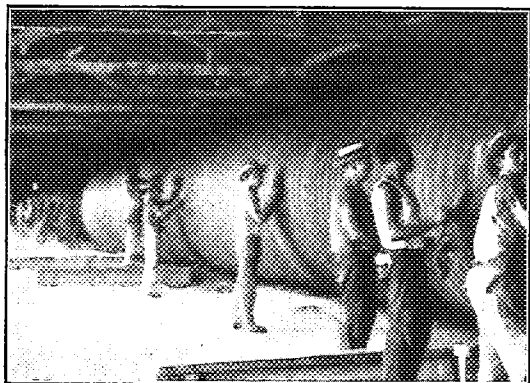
Fabrication des éléments de tubes : b, peinture d'un élément.
